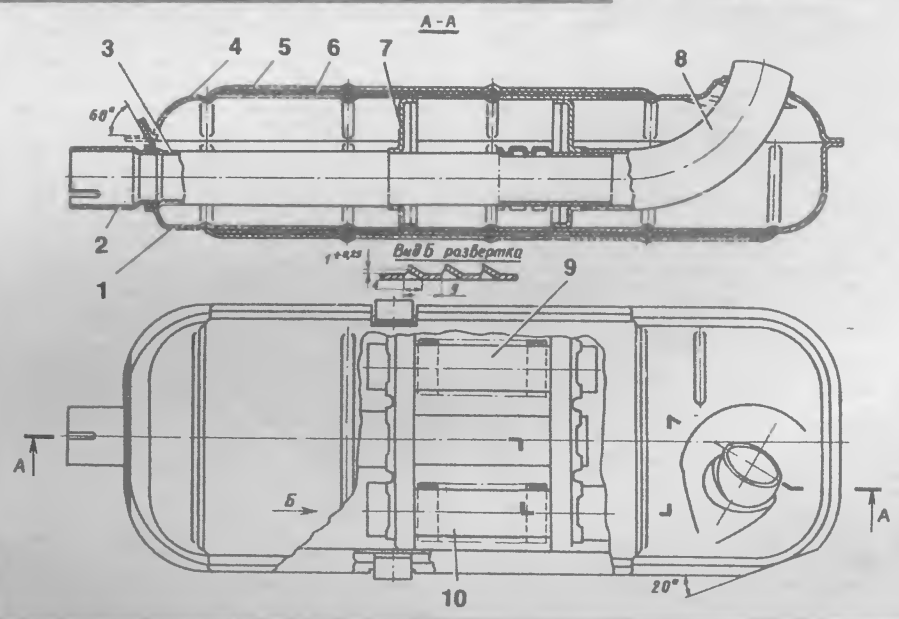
Глушитель «Москвича-412ИЗ» и «2125»: 1 — корпус (1,2); 2, 3 — кожухи (0,7); 3, 6 — асбестовые прокладки (2); 4 — перегородки (3 шт. 1); 5, 8 — отводящий и подводный патрубки (48 1,4); 9, 10, 11 — перфорированные трубы (45 1,4); 11 — заглушка (2); 12 — отводящая труба (45 1,4). В скобках указаны толщина листа или наружный диаметр и толщина стенки трубы в миллиметрах.
